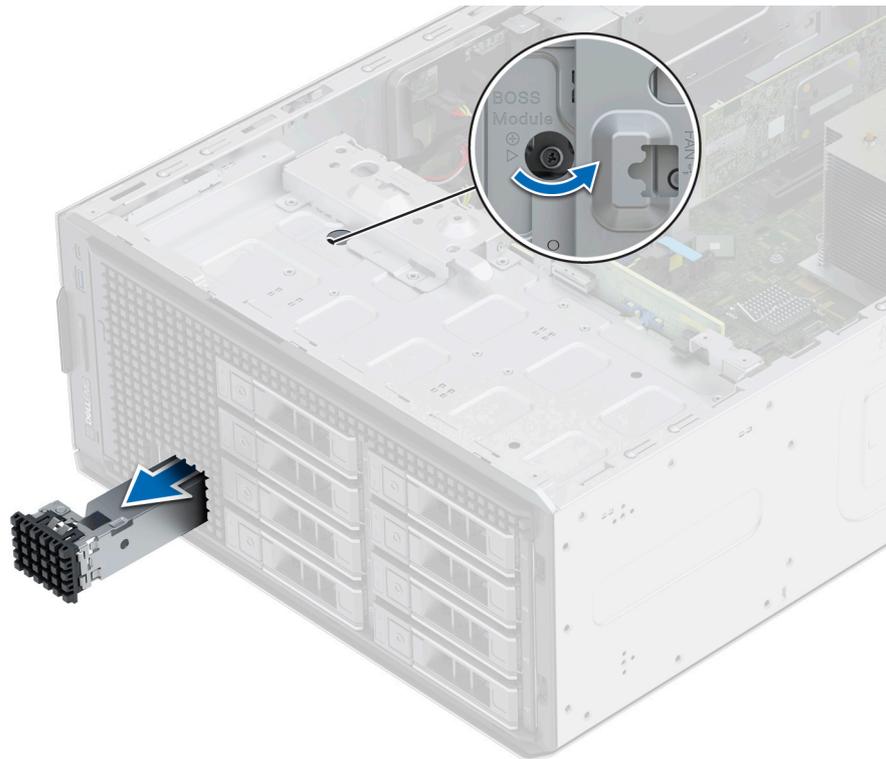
Entfernen des Platzhalters aus dem BOSS-S2-Modul
